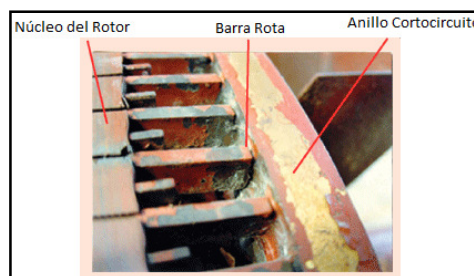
Rotor de Jaula de Ardilla con barra rota.
